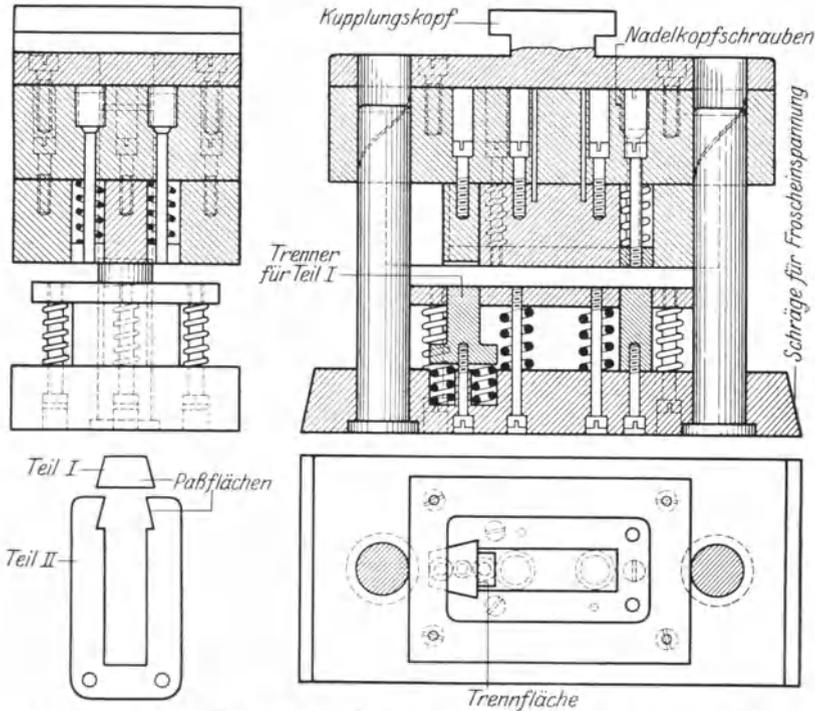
Komplettschnitt mit Trenner für Transformatorbleche.
